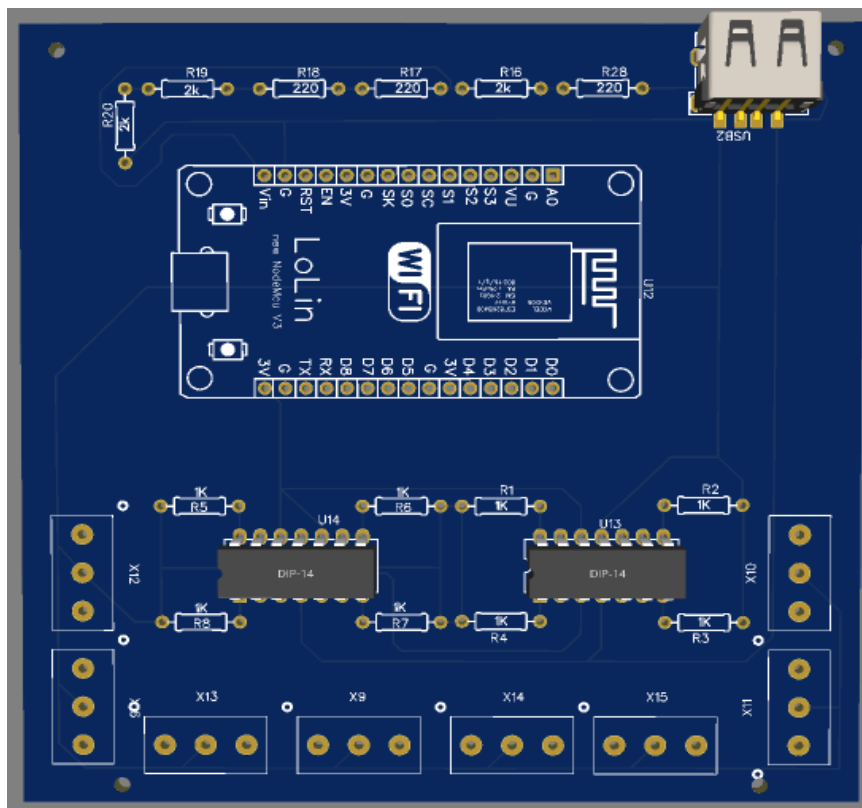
Diseño de PCB del dispositivo H2O (vista superior)
